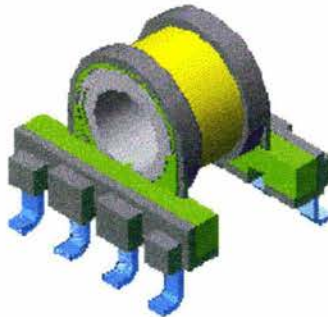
Moldeo del polímero que da forma a una segunda bobina (Pieza E). (Cortesía de Midcom Inc.)
